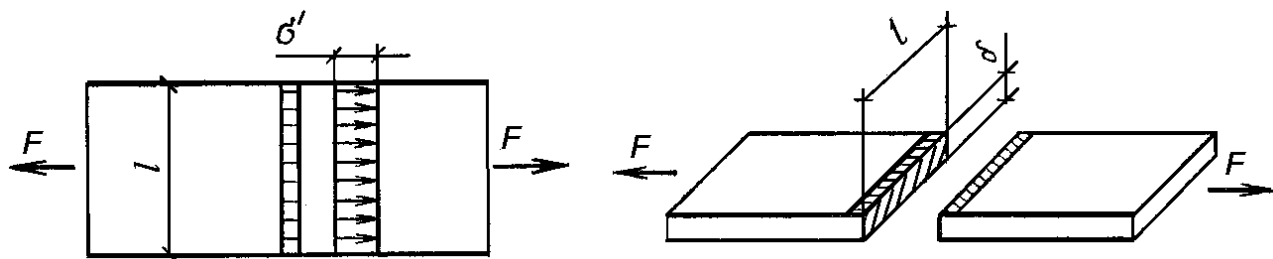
Схема нагружения стыкового сварного шва поперечной силой F
